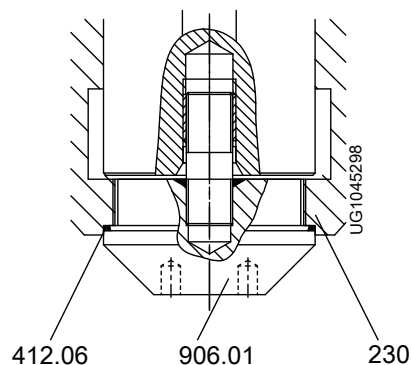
Laufradbefestigung M75 × 2 (für die Hydraulik E 200-401), M100 × 2 (für die Hydraulik K 350-710)
